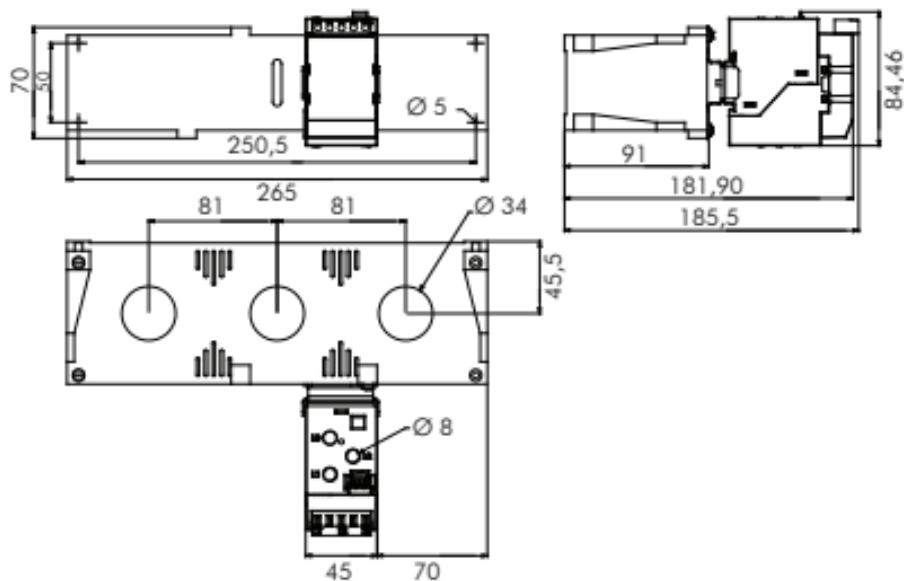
Dimensiones UMCT 6 (sin accesorio barramiento) (mm)
